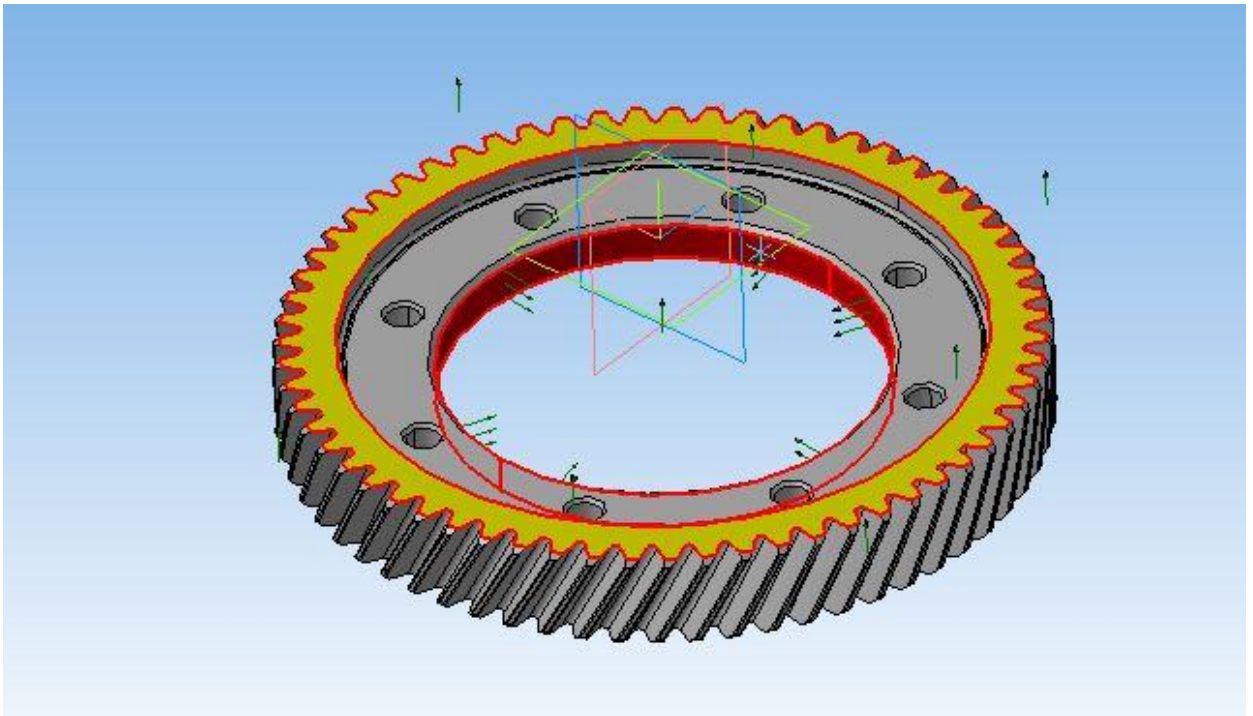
Фиксация шестерни в зажимном приспособлении
